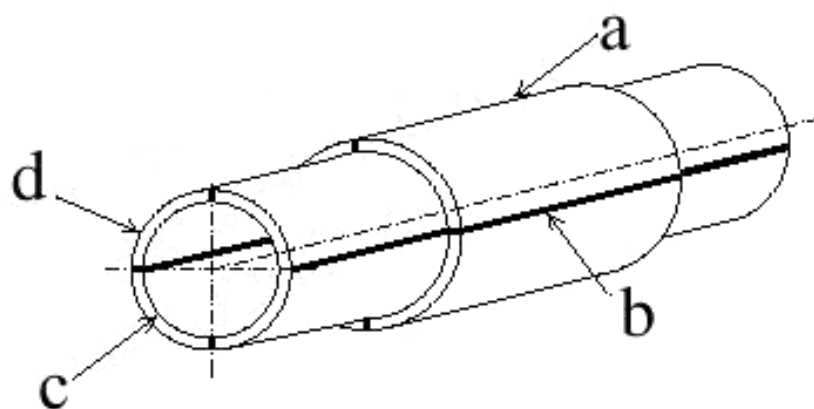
Позиции (от а до d) отбора образцов из соединений, выполненных раструбной сваркой с закладными нагревателями (неприменимо для седелок)
